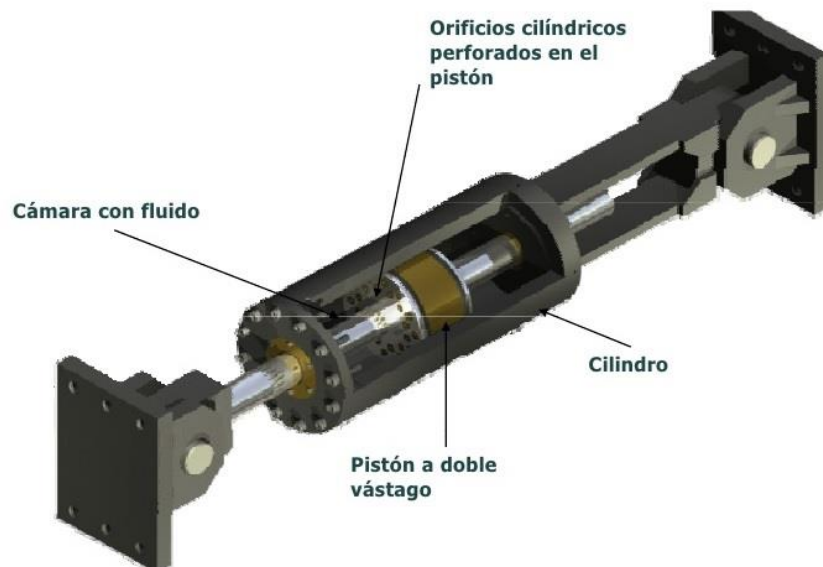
Partes principales de un disipador viscoso (de la Llera, 2010)
